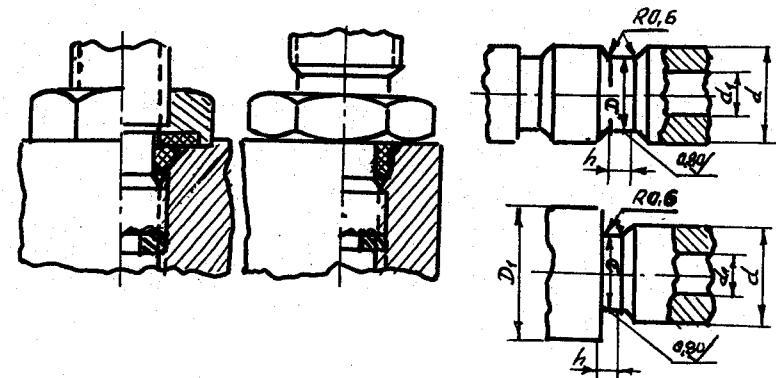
Способы уплотнения и обработки ввертных деталей
